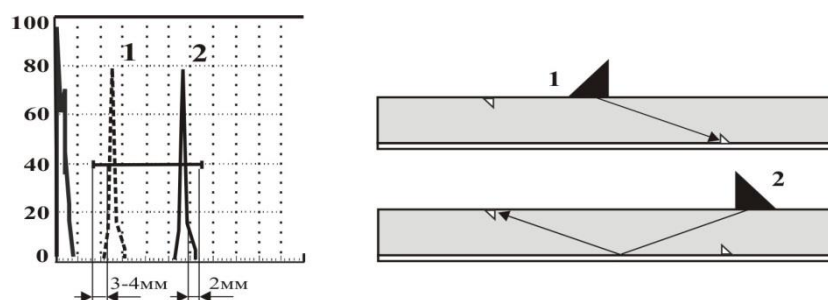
Схема настройки строб-импульса при контроле равнотолщинных сварных соединений труб
